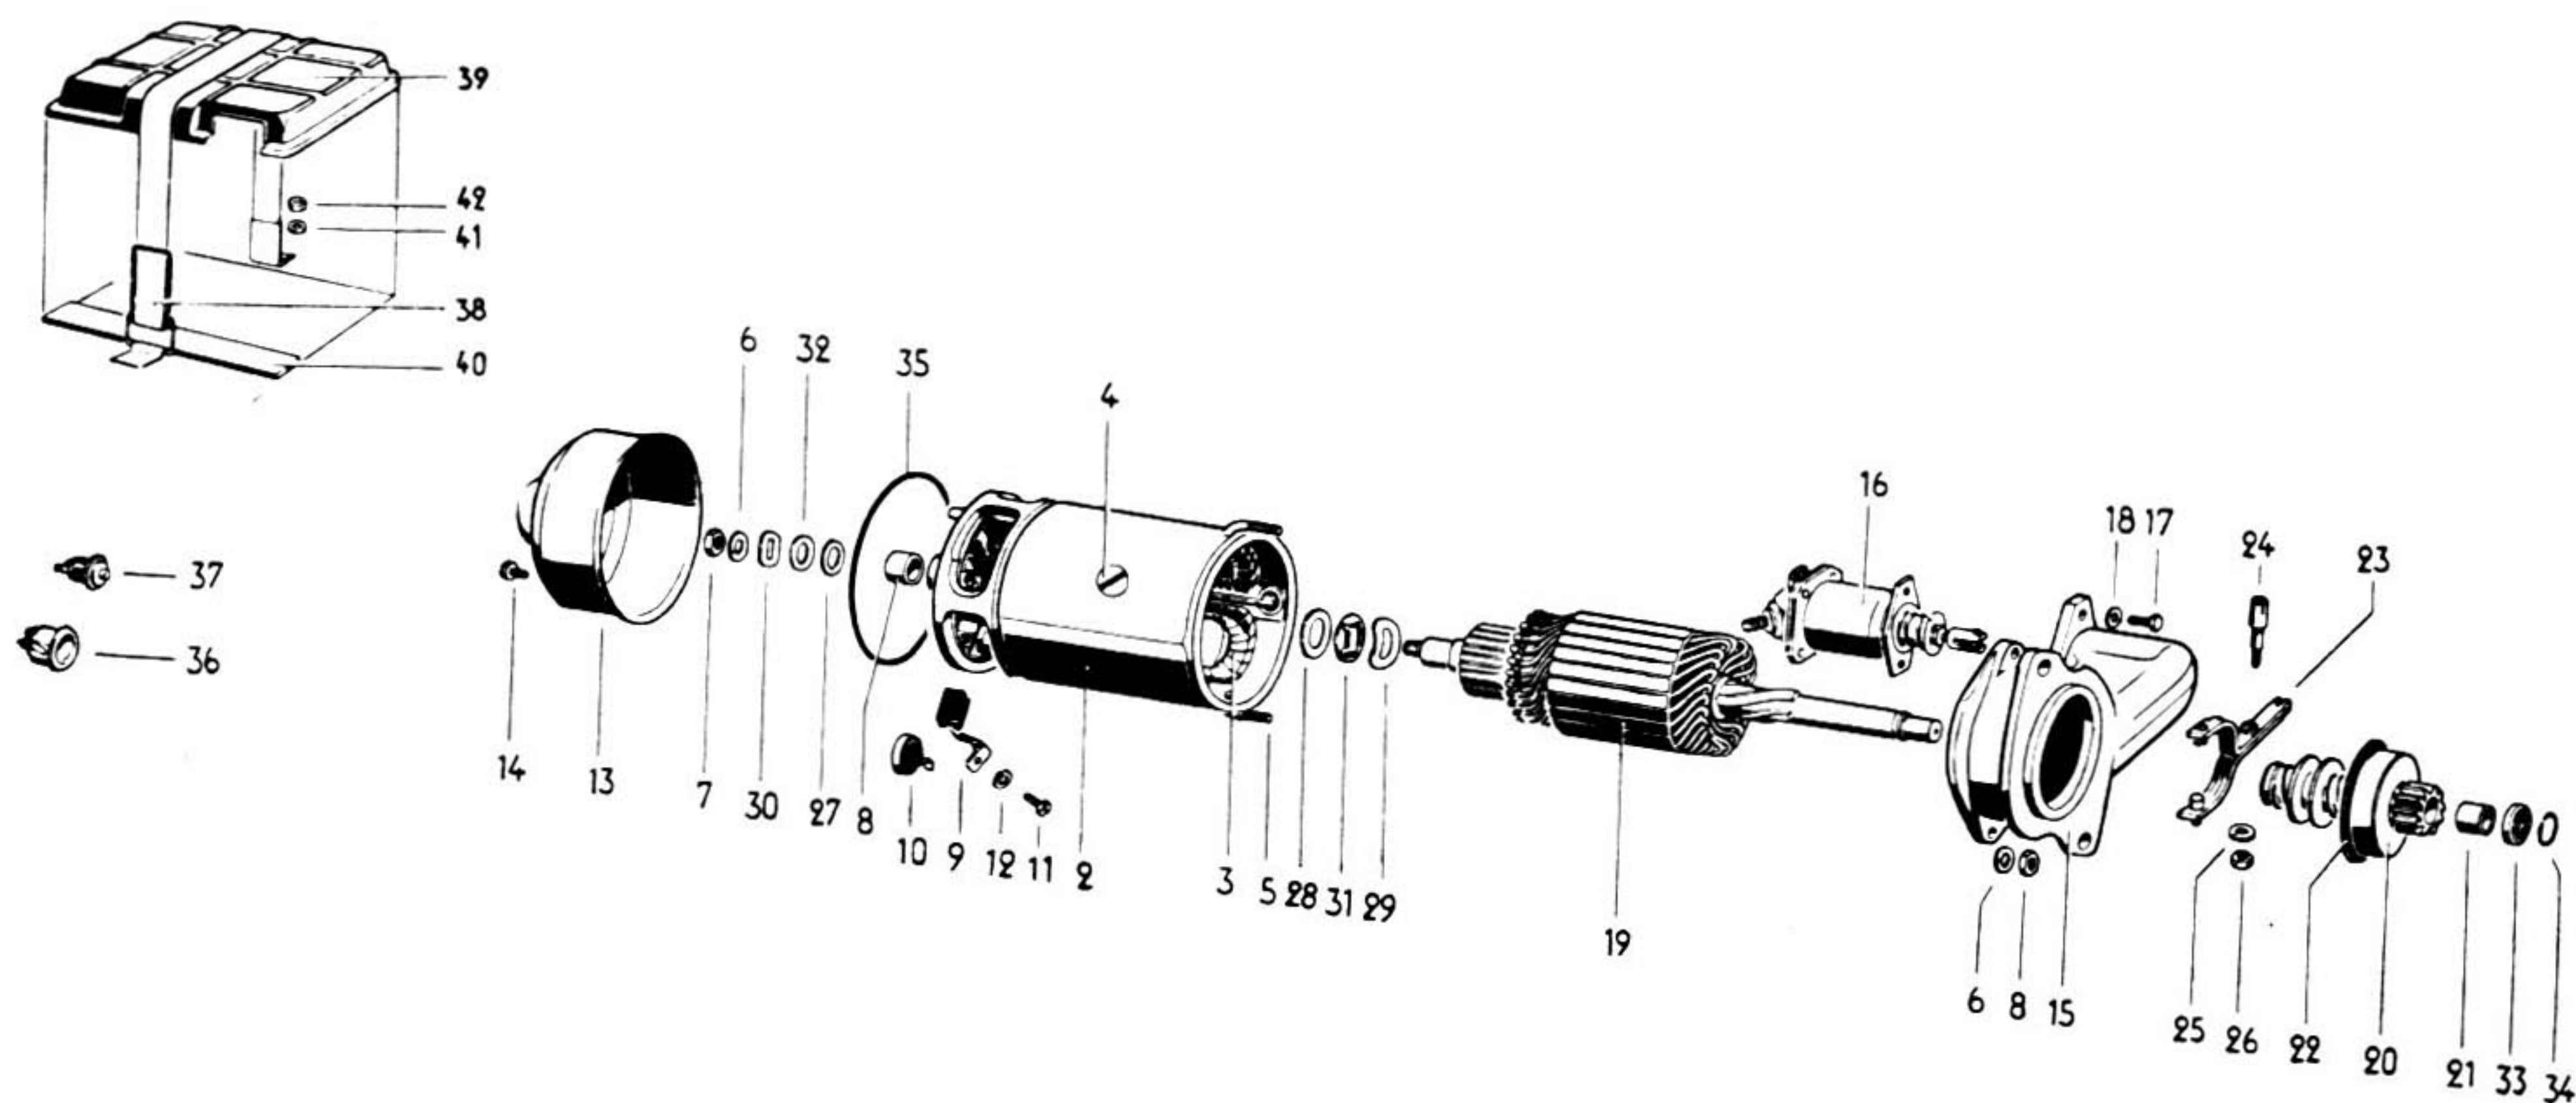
S — O motor de partida Bosch desmontado e a caixa da bateria
